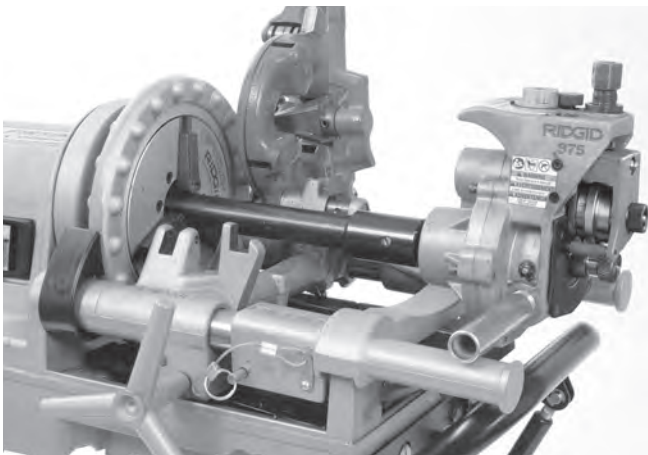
Ranuradora a rodillos combinada 975 correctamente montada en la máquina roscadora Compact 300
